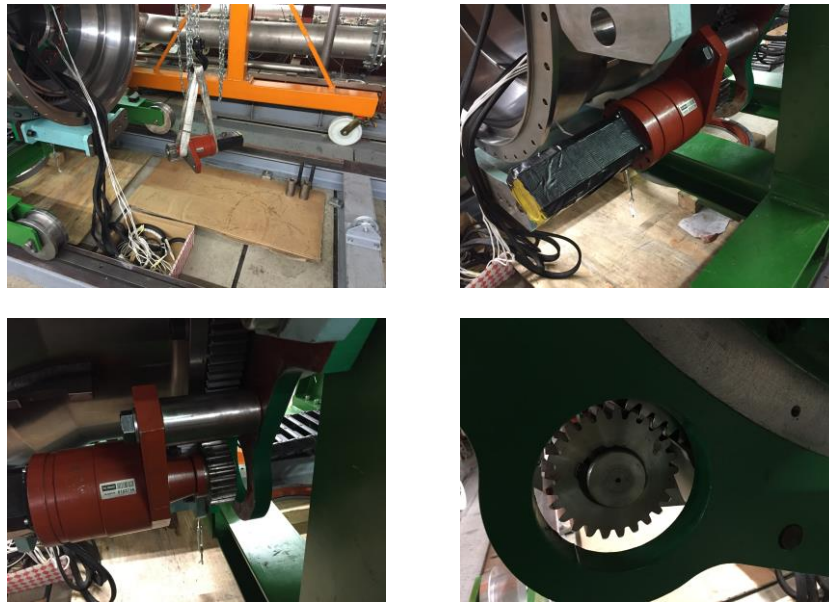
Fotoaufnahmen von der Montage des Bwd-Traversiermotors.
